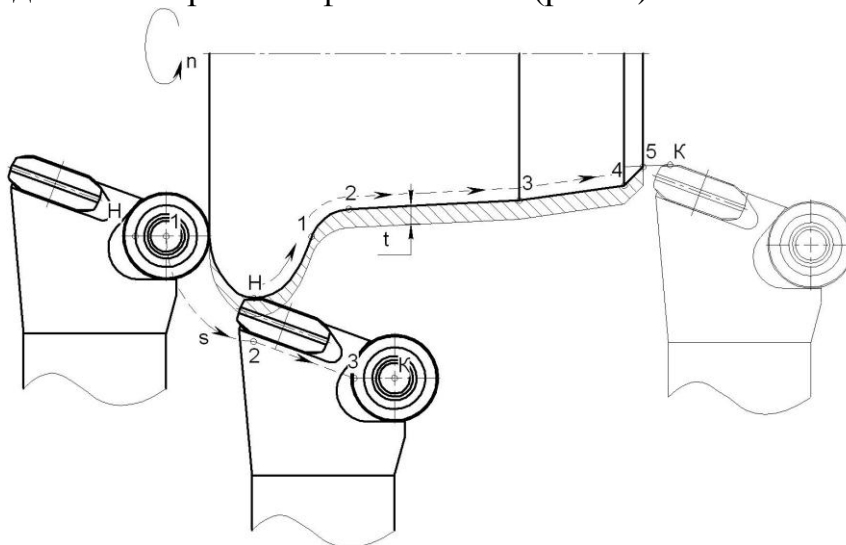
Схема обработки поверхности колеса от гребня к фаске
